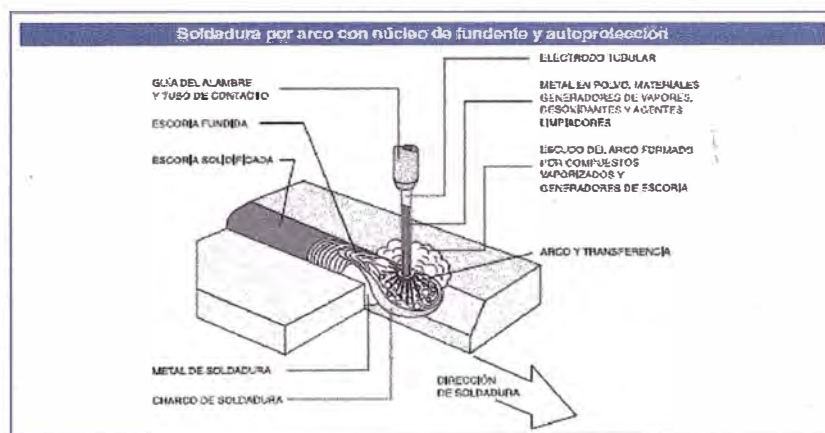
Esquema Proceso FCAW sin gas (Fuente: Manual de Soldadura Indura)
